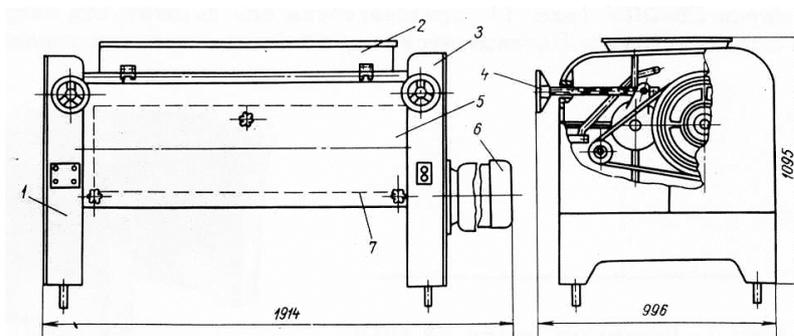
Общий вид вальцовки марки Е8-ОПУ для творога: 1 – боковина левая; 2 – бункер; 3 – боковина правая; 4 – механизм регулирования зазора; 5 – рабочие валки; 6 – привод; 7 – нож (показана зона расположения)
